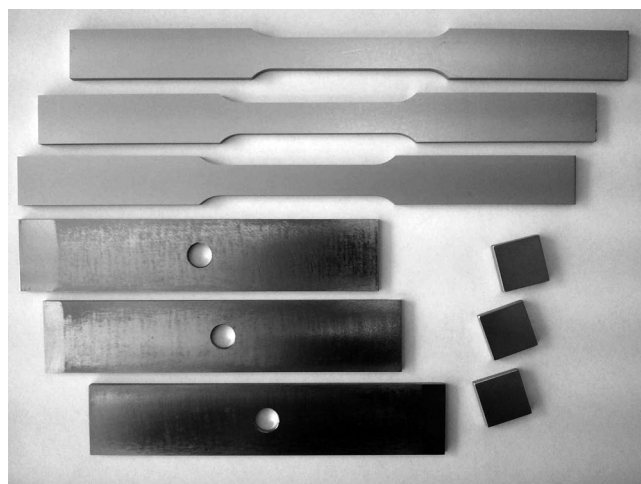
Общий вид образцов для испытаний на усталость и на растяжение.
